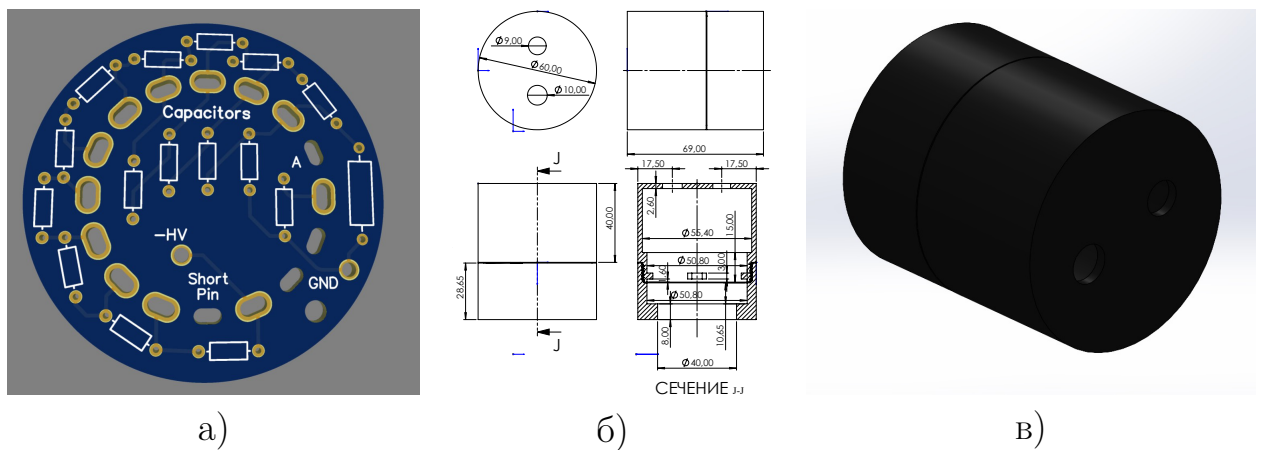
а) Плата делителя напряжения ФЭУ. б) Чертеж корпуса для делителя напряжения ФЭУ. в) 3D-модель корпуса для делителя напряжения ФЭУ. В отверстия помещаются BNC- и SHV-разъемы (сигнальный и питания соответственно), а сам делитель напряжения размещается и фиксируется в специальном пазе на противоположном торце детали.
